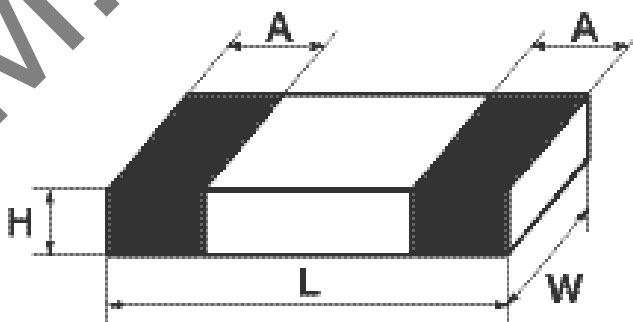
Зовнішній вигляд резистора 1206 [21]
